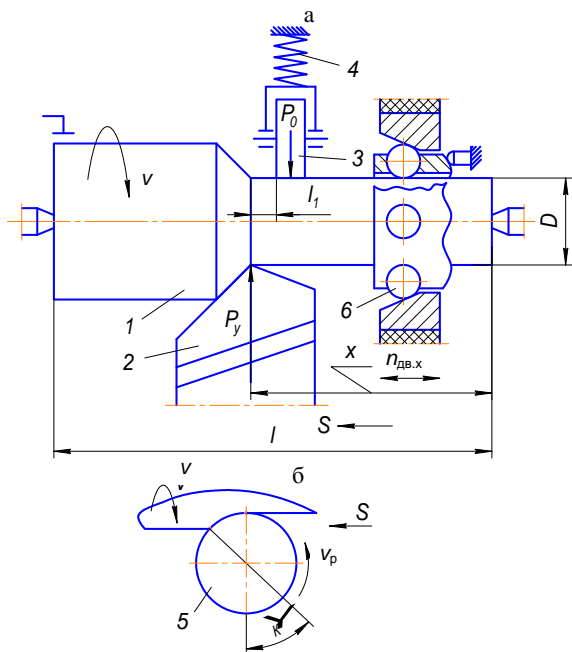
Схемы обработки: а – призматическим резцом и ИСВ; б – резцом с МОРК; 1 – заготовка; 2 – призматический резец; 3 – ролик; 4 – упругий элемент (пружина); 5 – резец с МОРК; 6 – виброобкатывающая головка; $v, v_{п}, S$ – направление вращения заготовки, резца с МОРК и перемещение резца соответственно; $n_{дв.х}$ – возвратно-поступательное движение сепаратора с шарами при ИСВ; ψ_k – угол контакта чашечного резца с заготовкой; P_y, P_0 – радиальная составляющая силы резания и усилие деформирования соответственно
